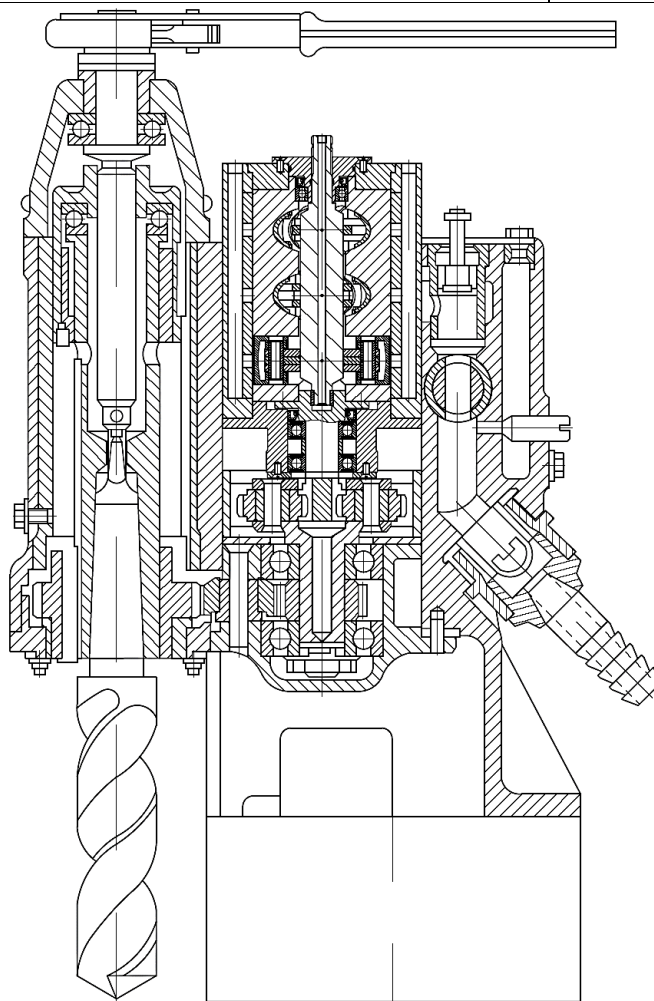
Модернізований свердлильний верстат СПС-50 з роторно-поршневим двигуном об'ємної дії із шарнірно-кулачковим механізмом руху
